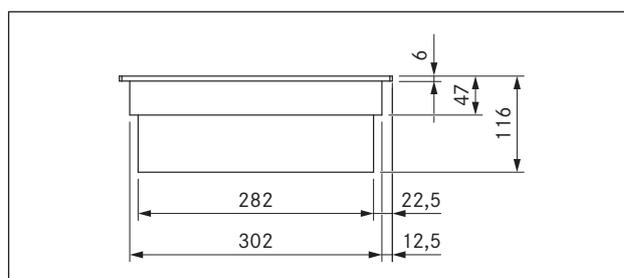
Dimensões do aparelho CKIW, vista frontal
